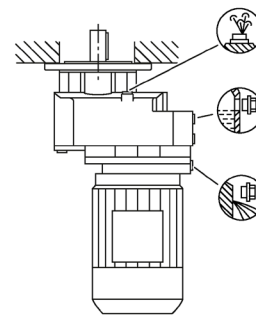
Einbaulagen für Stirnradgetriebe E Fußausführung Baugrößen 39 - 149
